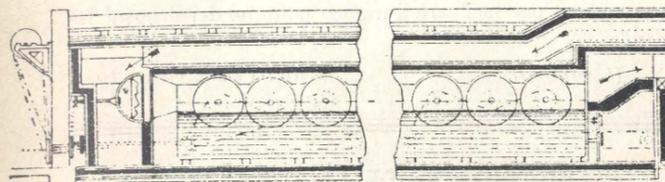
Apparecchio a dischi (sezione longitudinale).
